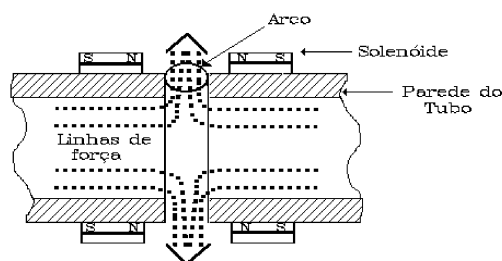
Soldagem de um Tubo por Arco Magneticamente Impelido.
